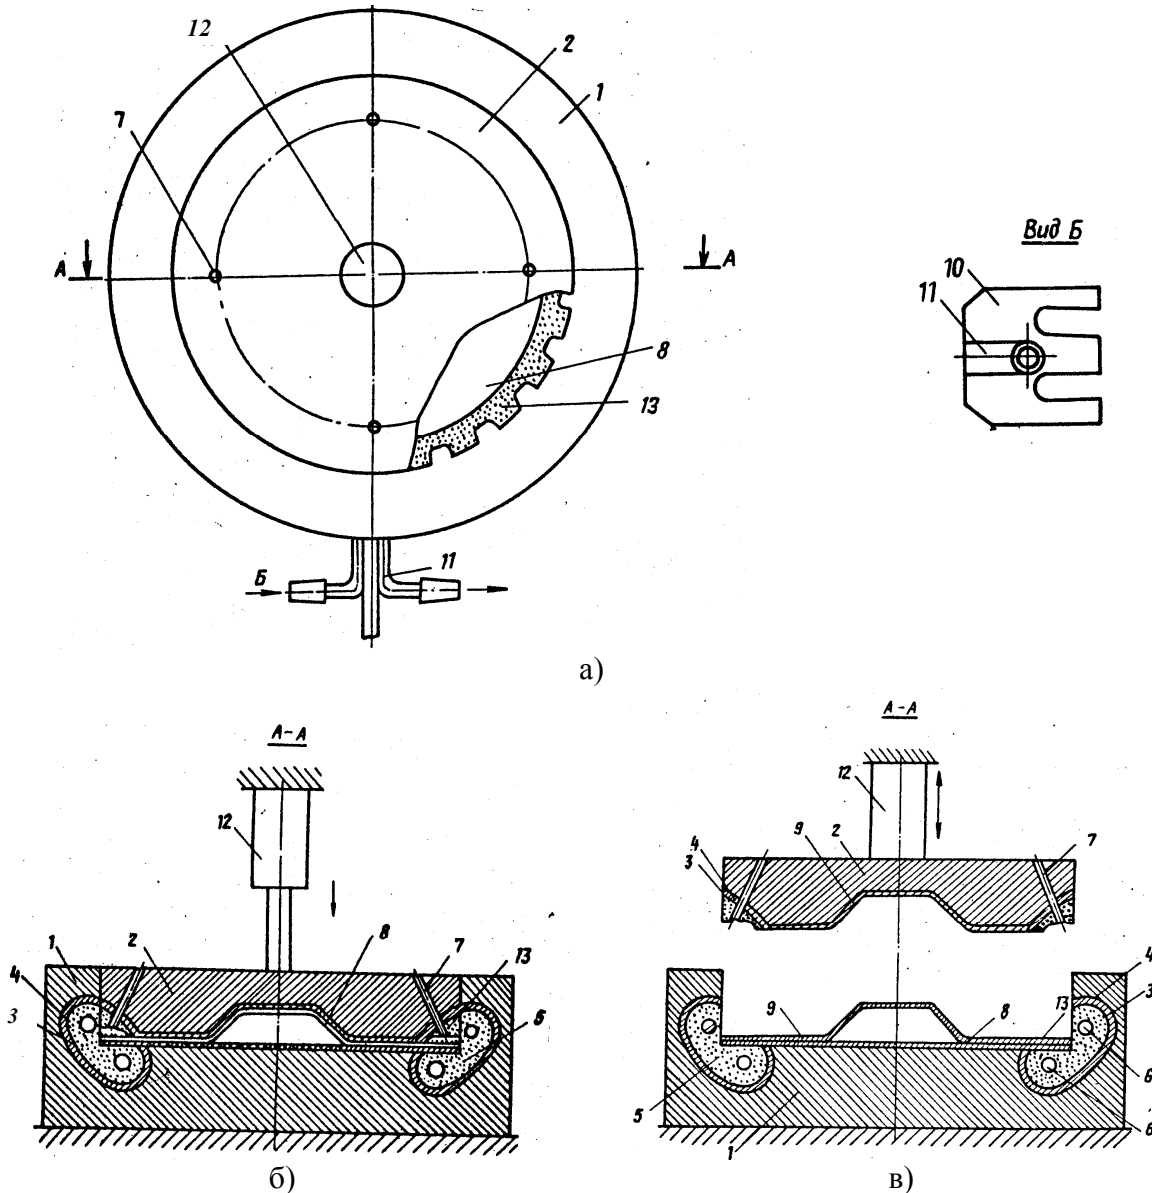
Пристрій для індукційного наплавлення тонких фасонних дисків:
